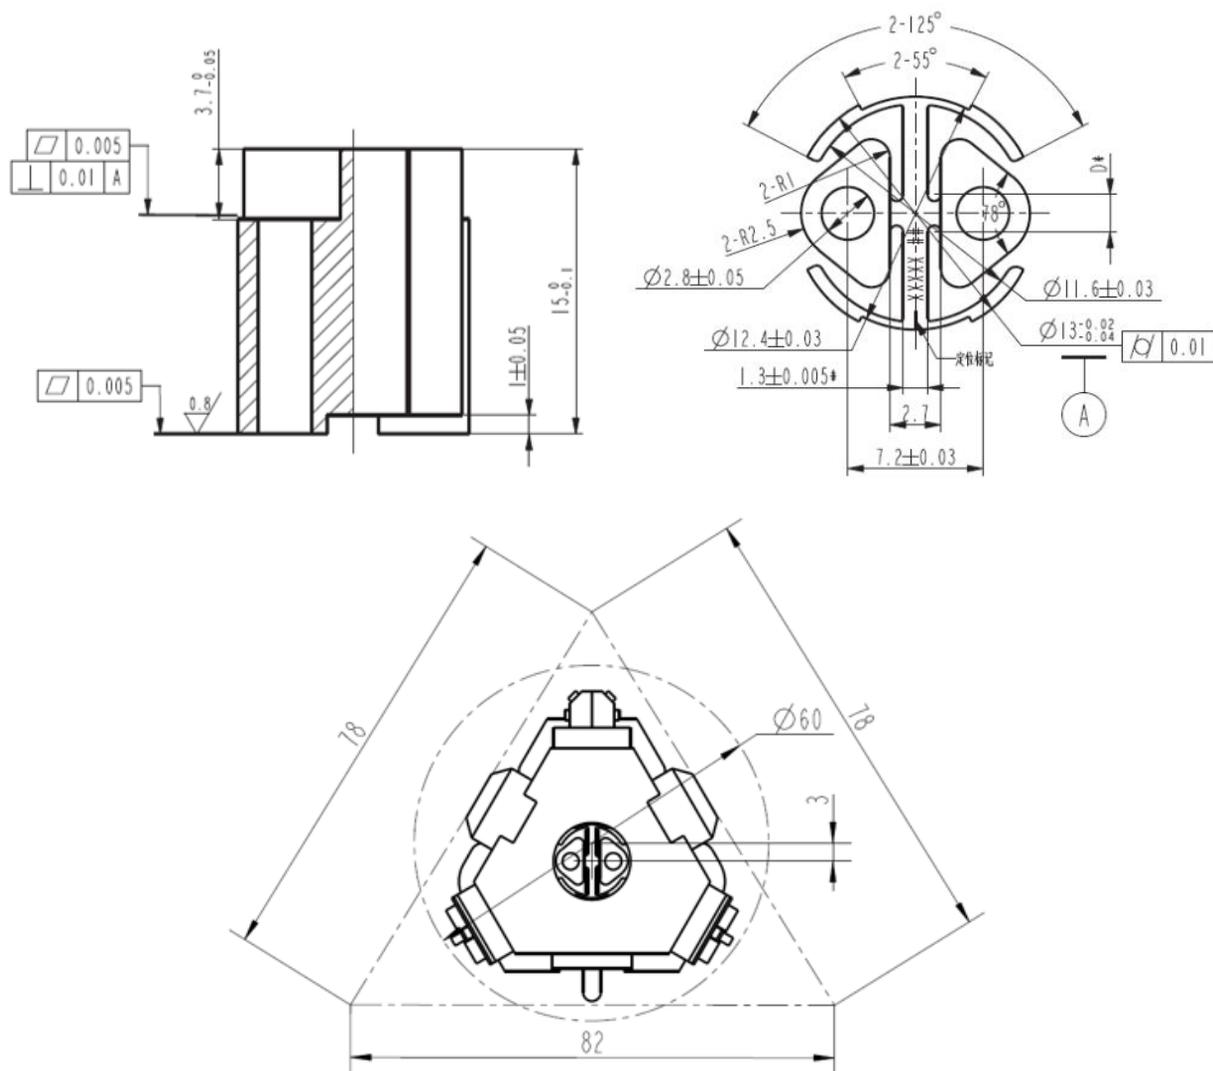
Габаритные размеры одноосного лазерного гироскопа
